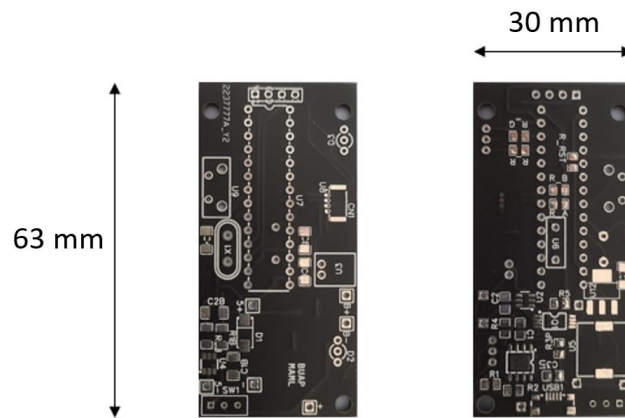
Tarjeta manufacturada y dimensiones. a) Capa superior b) Capa inferior.
